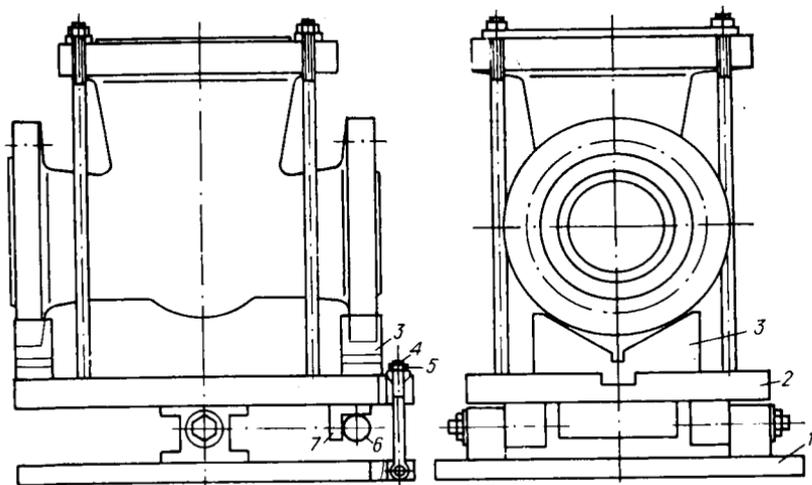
Приспособление для проточки зеркал клиновых задвижек:
